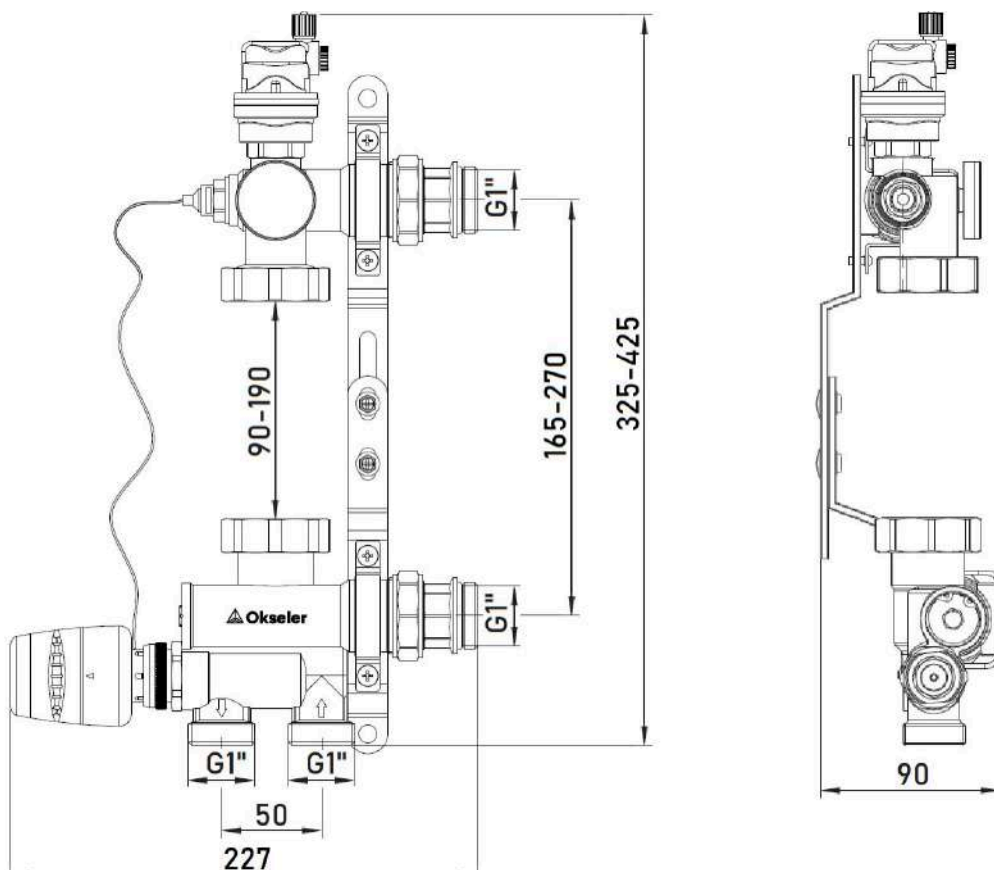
Габаритные размеры насосно-смесительного блока Oks001488
